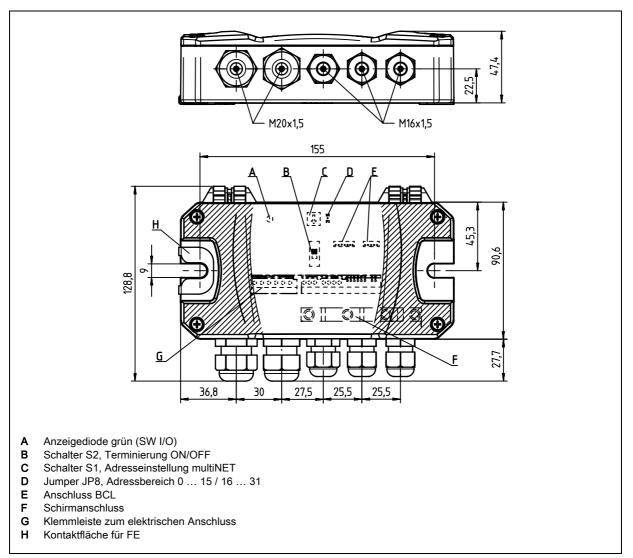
Maßzeichnung Klemmenbox MA 100
